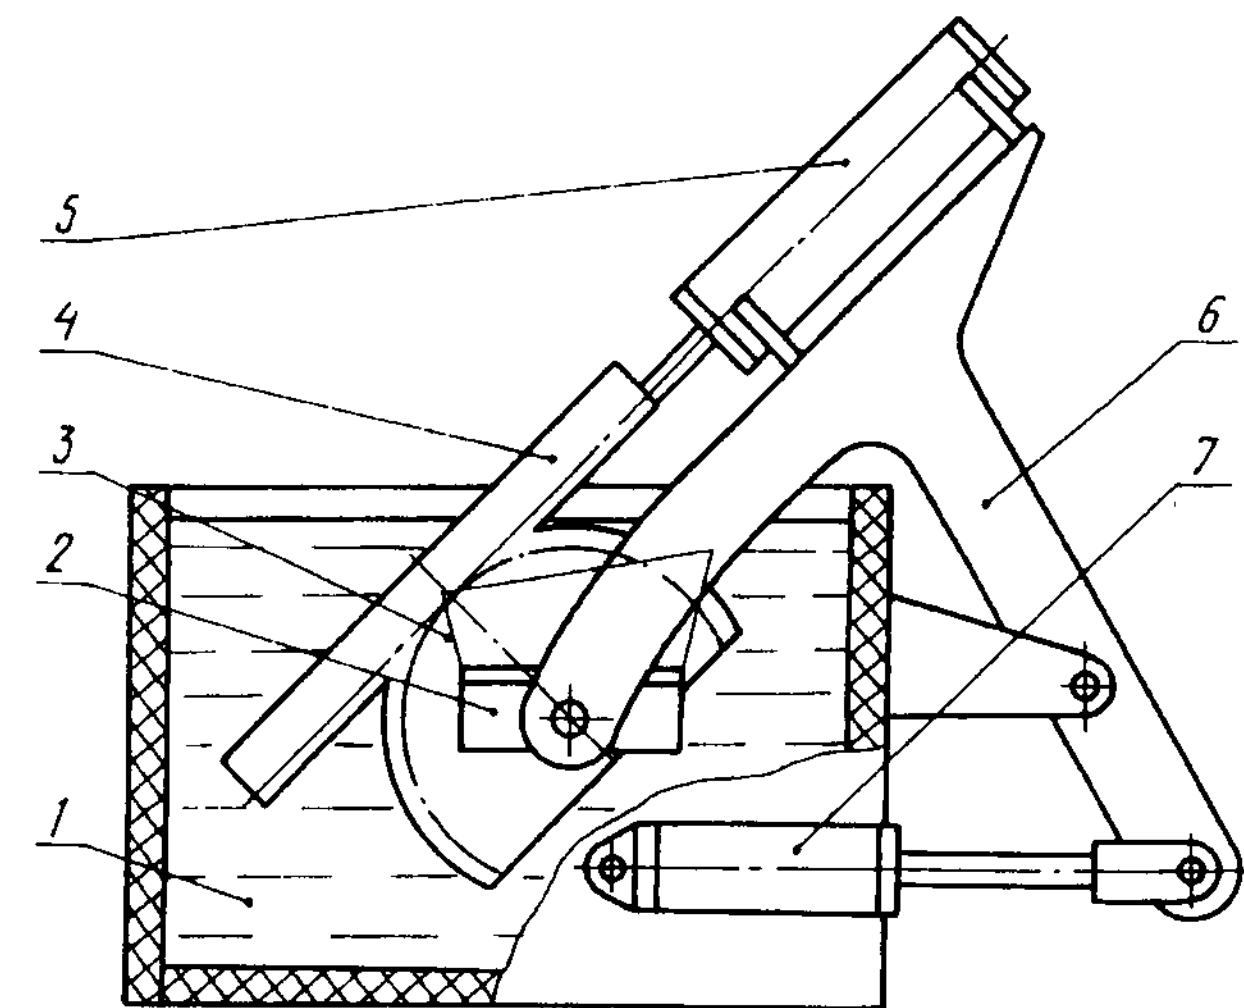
Стенд для контроля герметичности головки цилиндров
